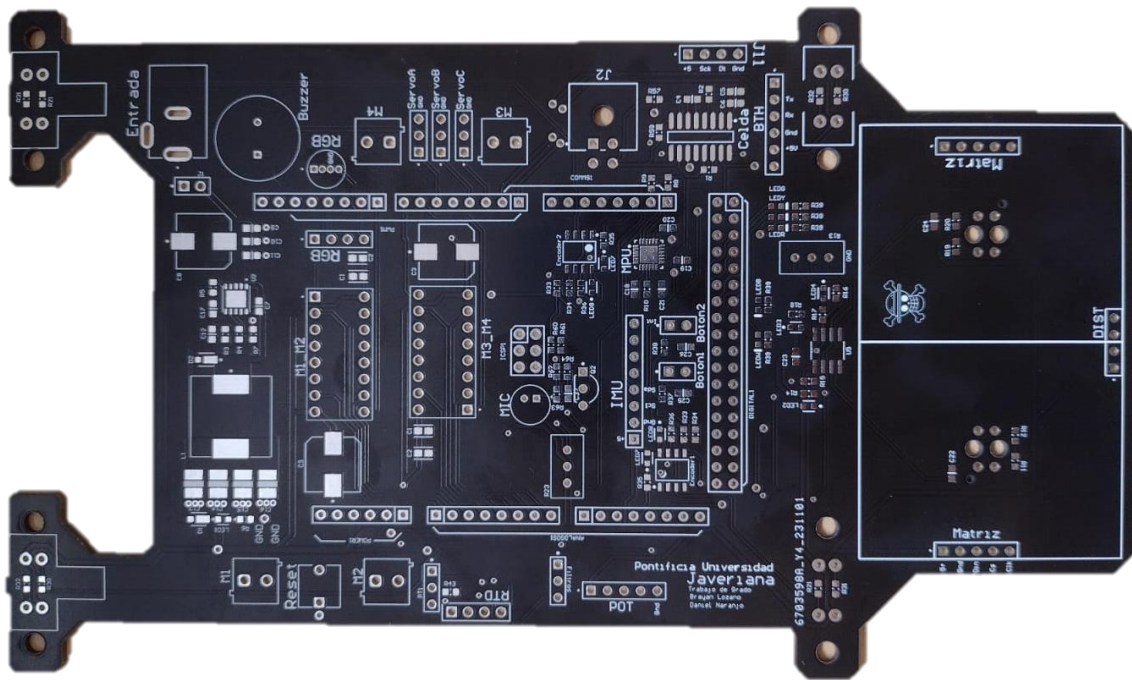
Vista superior del PCB fabricado versión 3 (Final)
